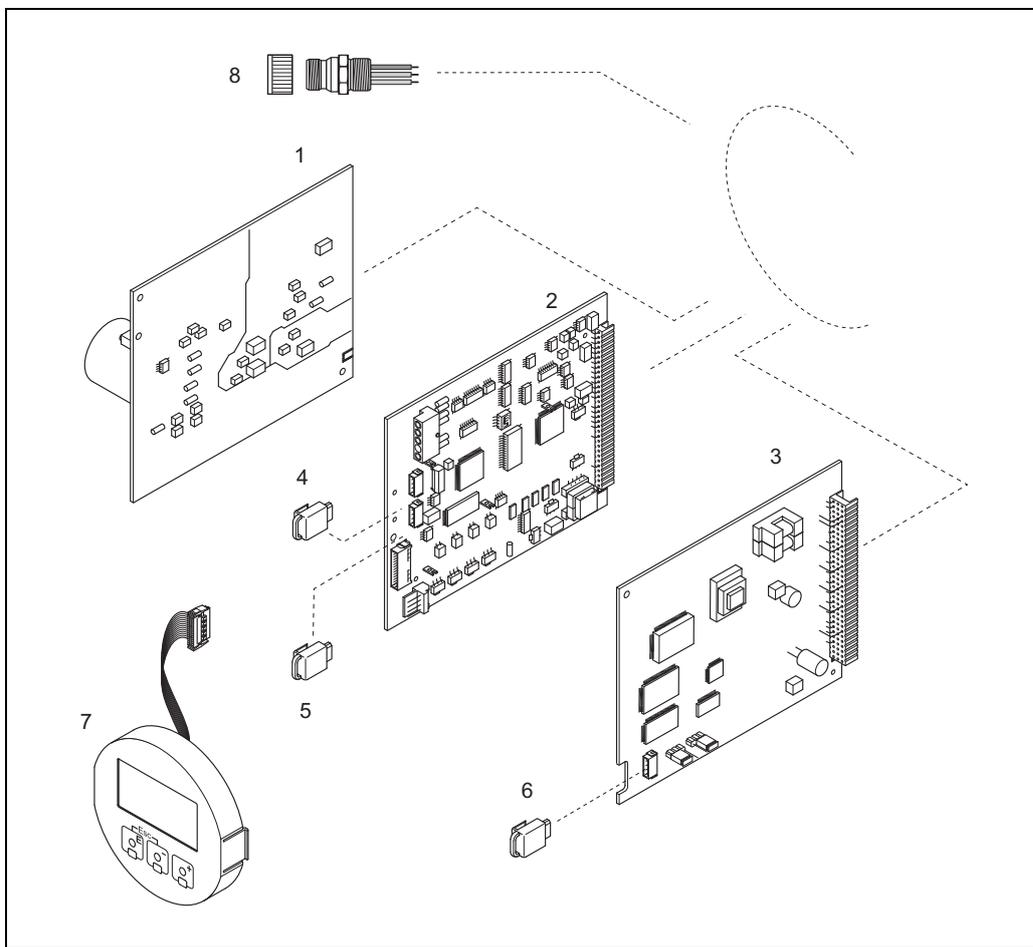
Запасные части для преобразователя Promag (полевой корпус и настенный корпус)
